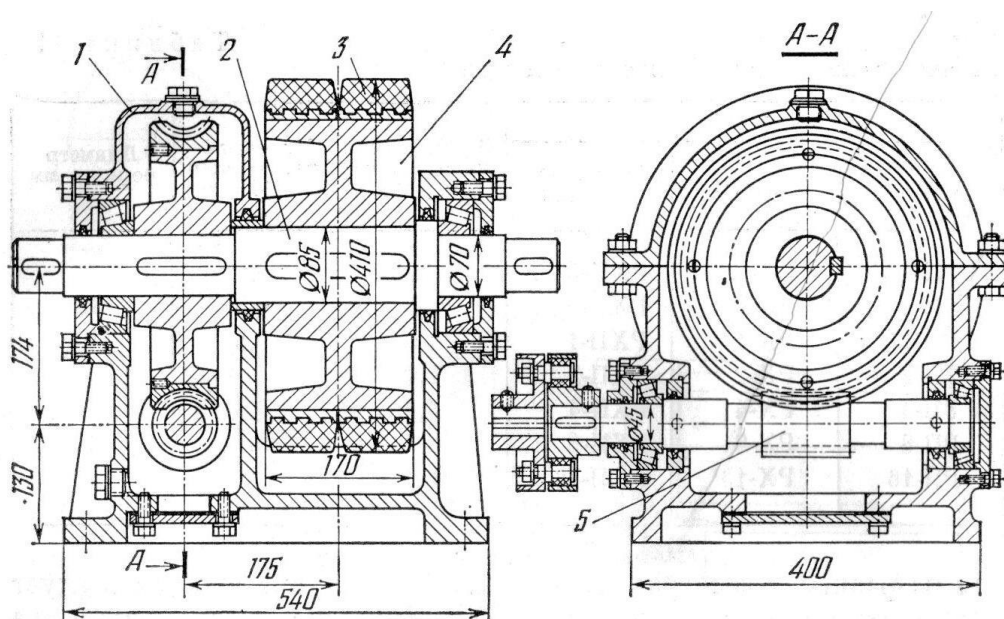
Приводная роlikоопора с червячным редуктором:
